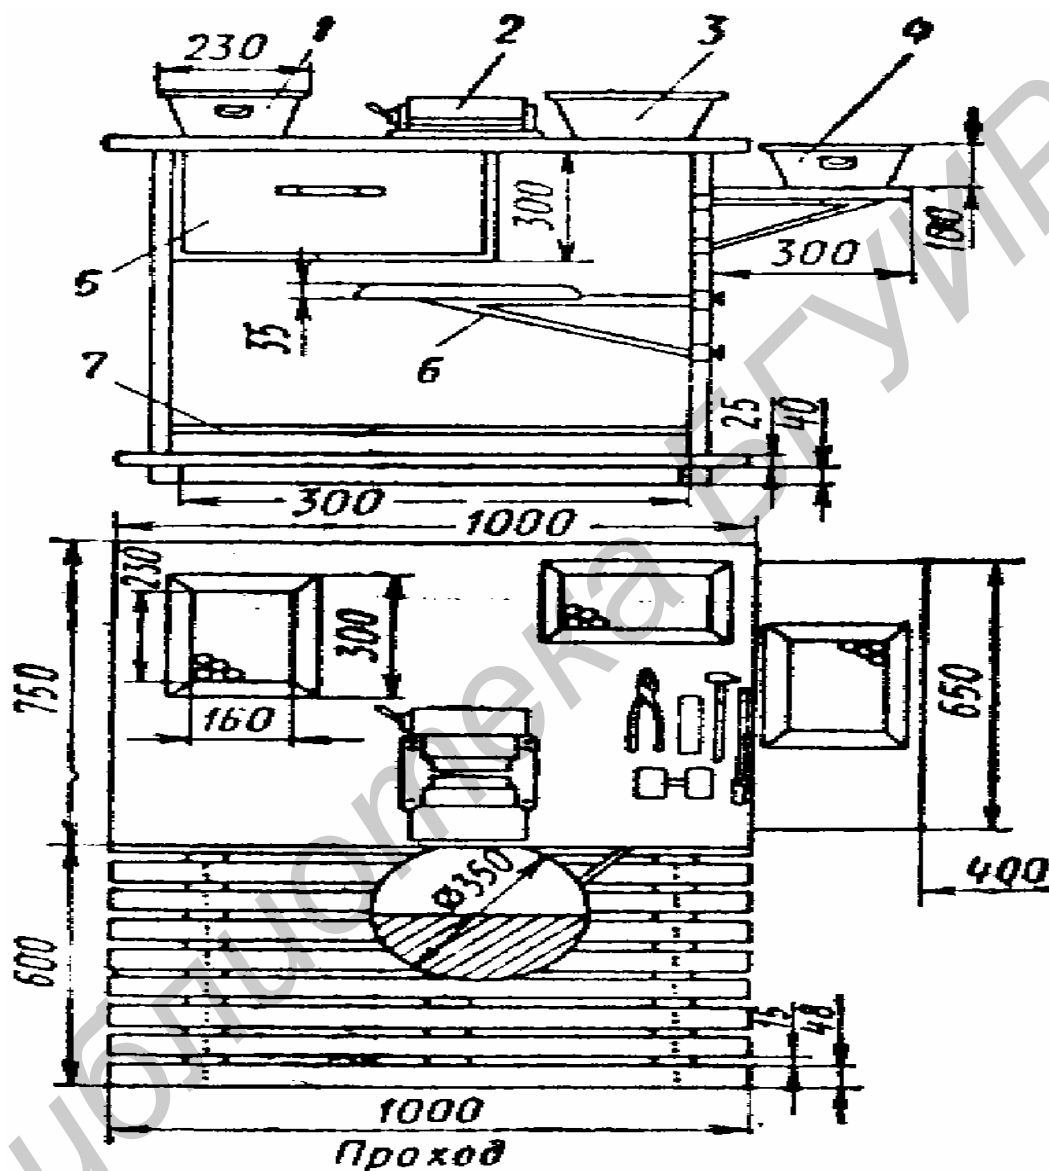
Схема планировки рабочего места слесаря-сборщика:
